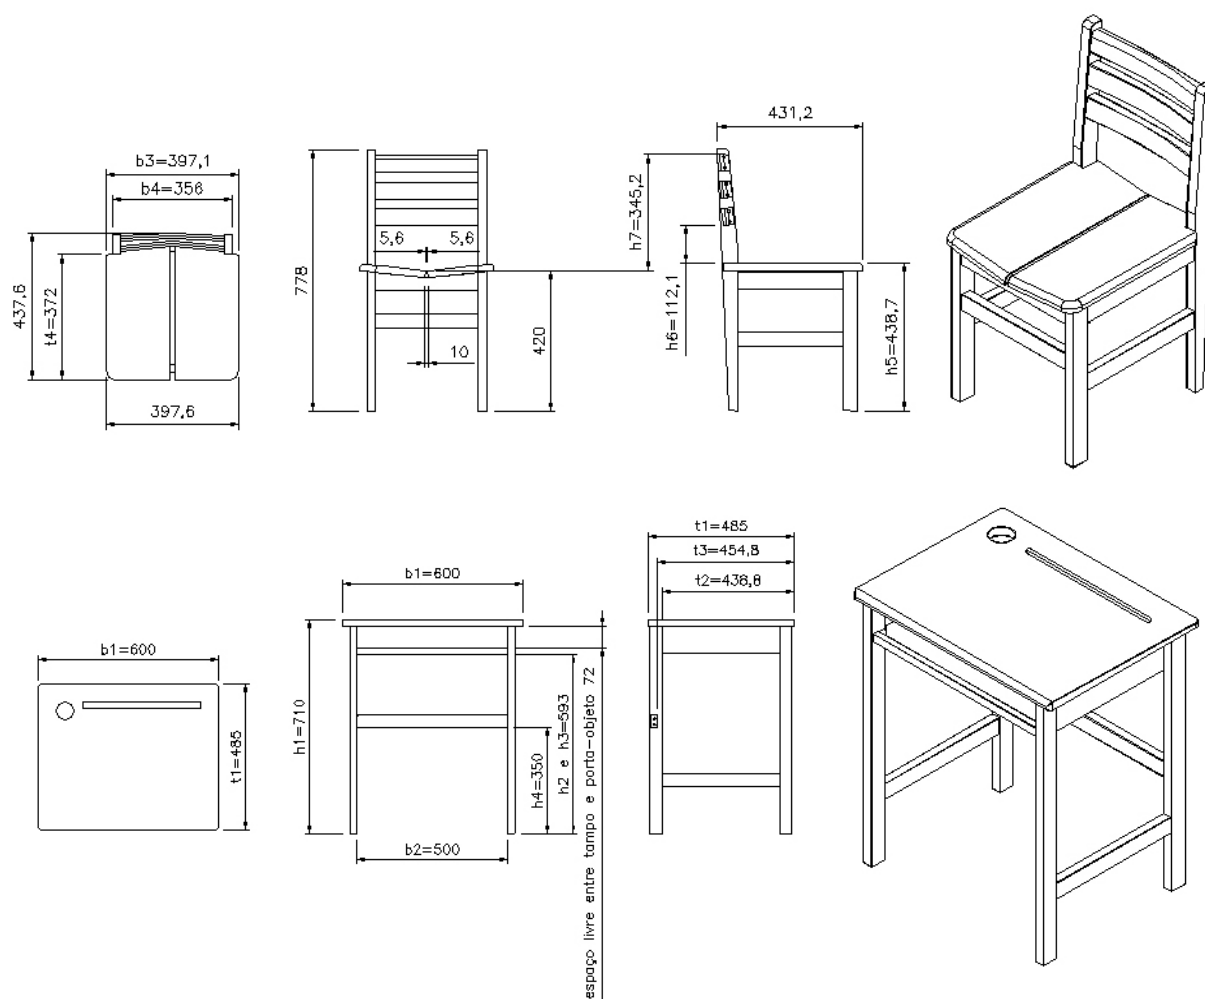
Dimensões do conjunto-aluno modificado em mm (planta, elevação frontal e lateral e perspectiva da cadeira e mesa escolar)
